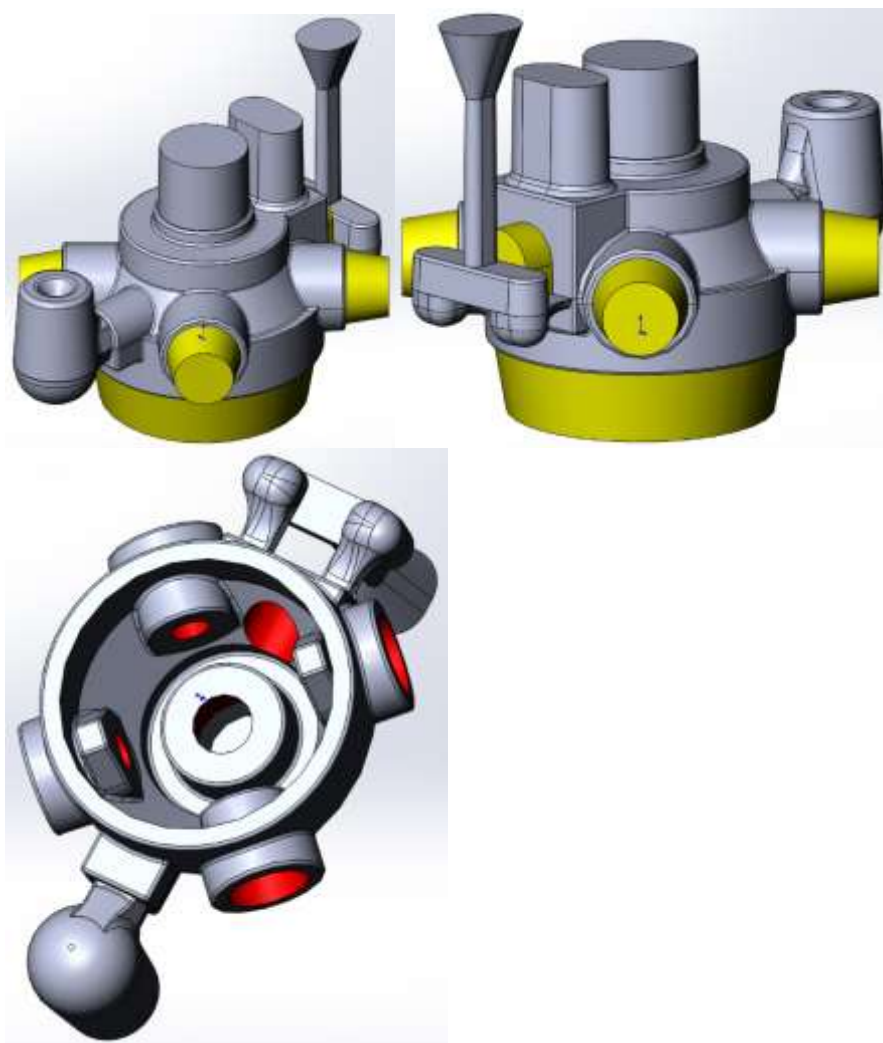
Отливка с литниковой системой, созданная в SolidWorks
